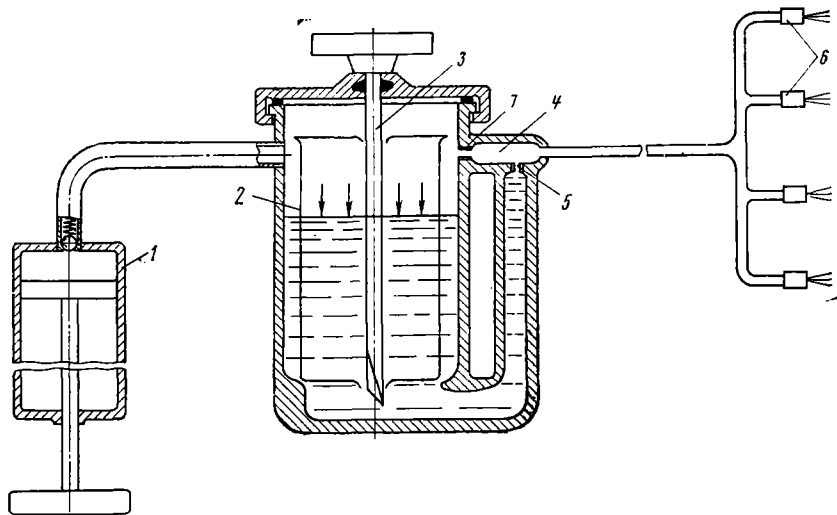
Схема приспособления для впрыска пусковой жидкости во впускной трубопровод двигателя
